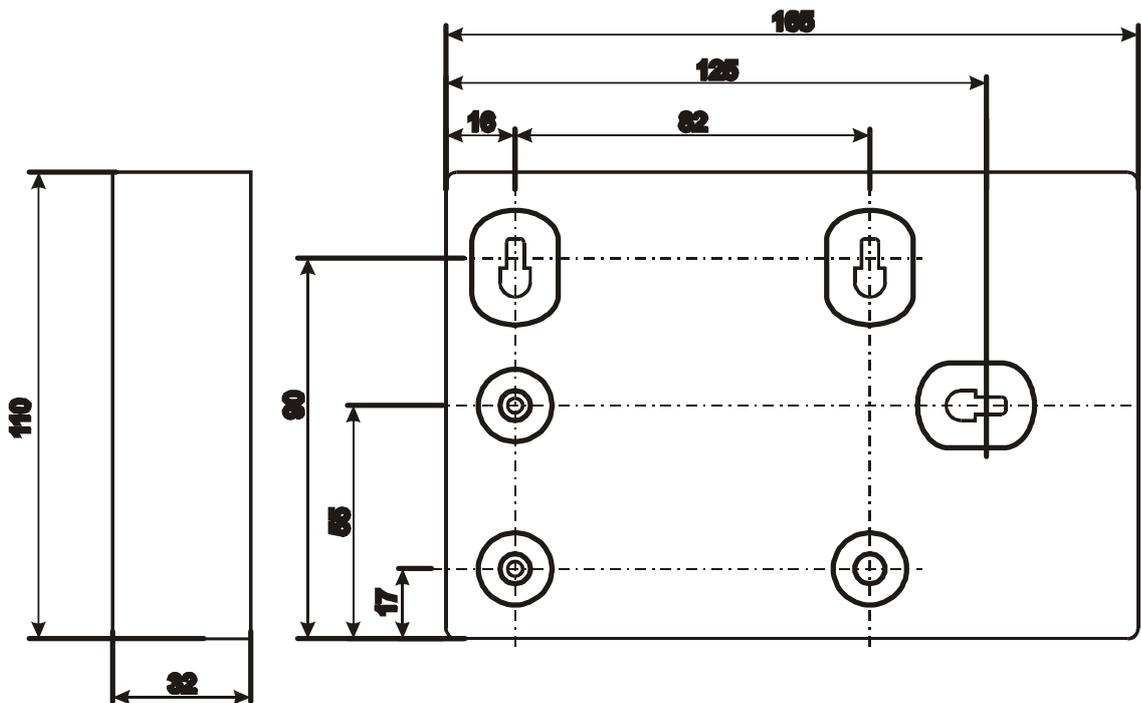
Габаритные и присоединительные размеры КА2 исп. IP20
